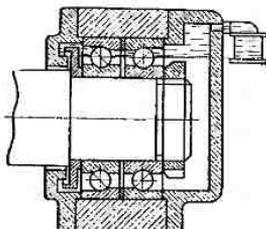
Сквонное отверстие в крышке корпуса подшипника
